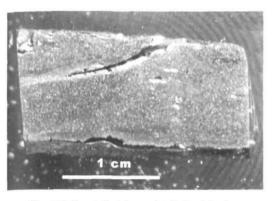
Macrografía de la zona de soldadura de la pieza.
